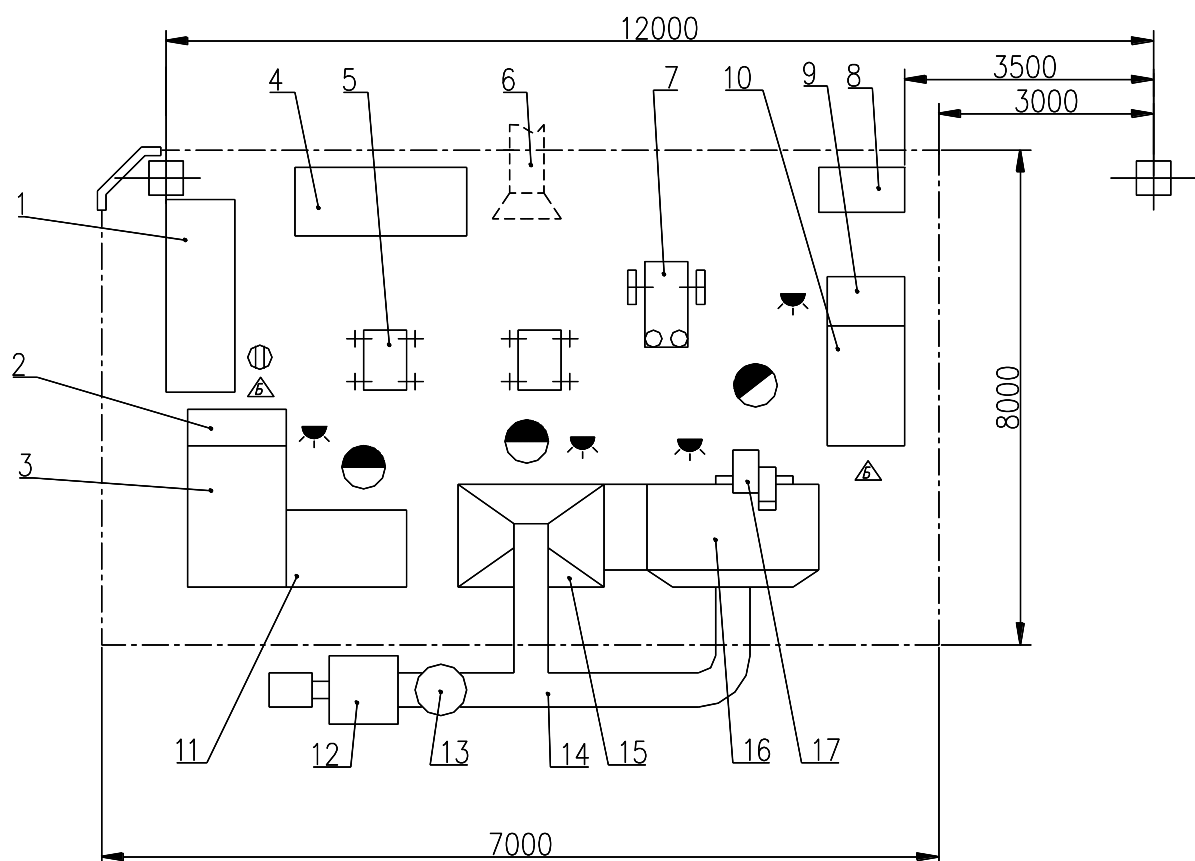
Схема компоновочная участка сварки
